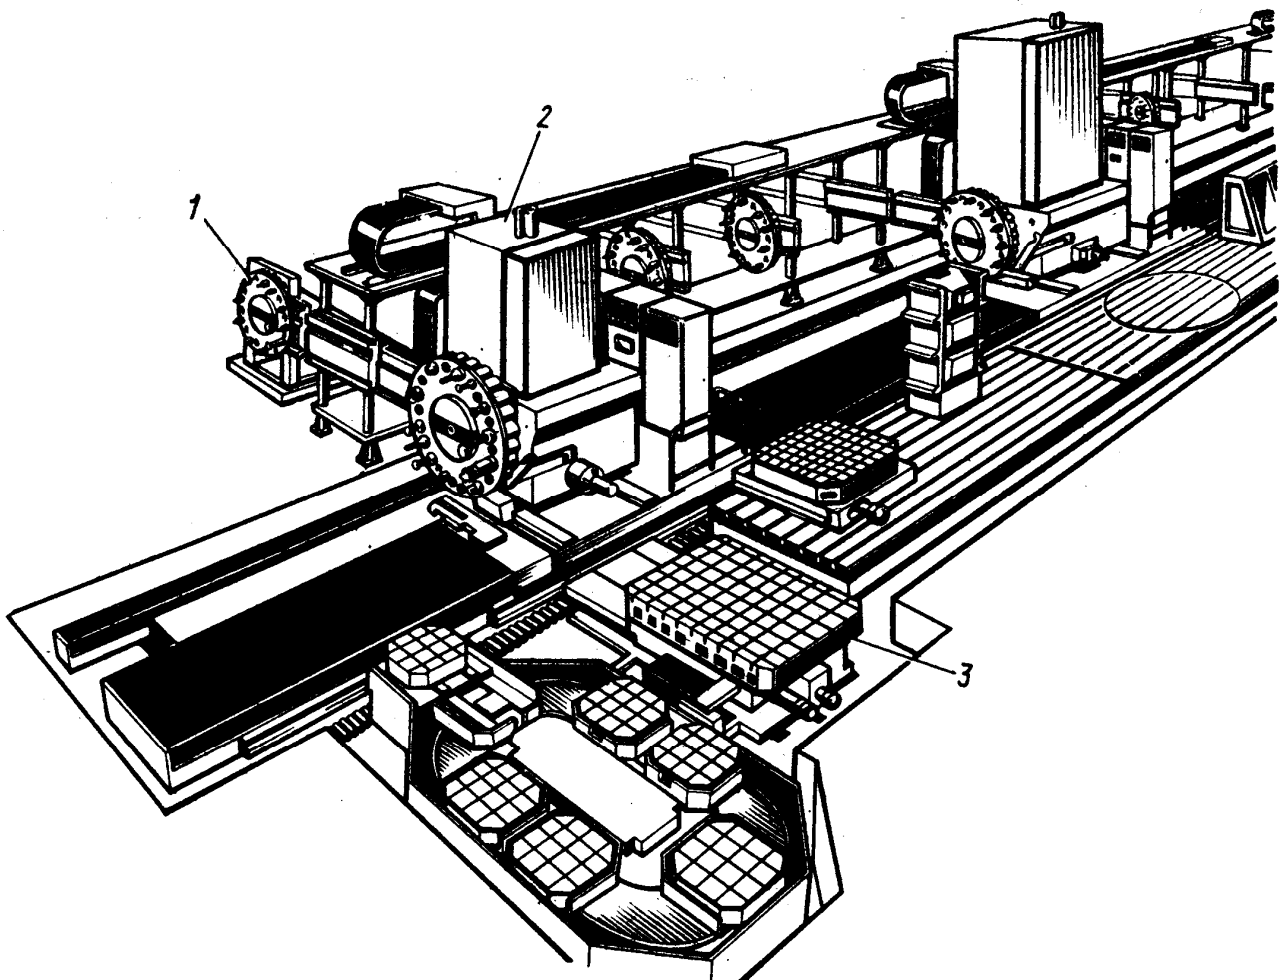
Модуль багатноменклатурного автоматизованого комплексу фірми Yamazaki (Японія) для оброблення корпусних деталей
